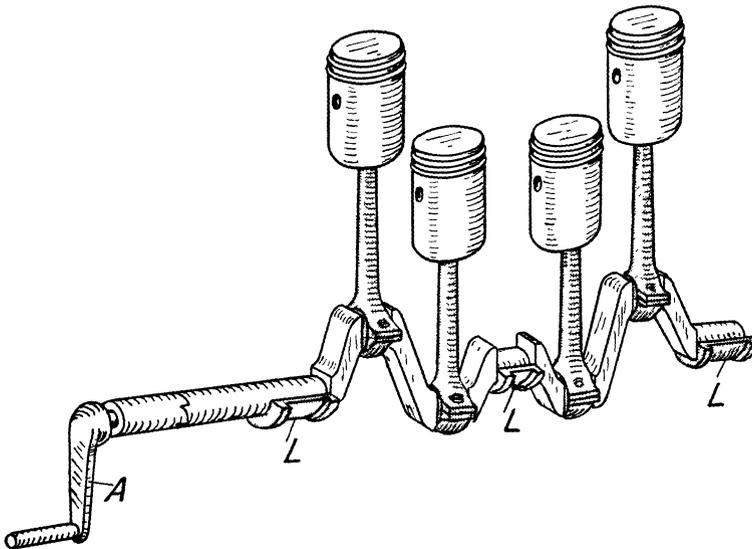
Kolben und Kurbelwelle eines Vierzylinders
